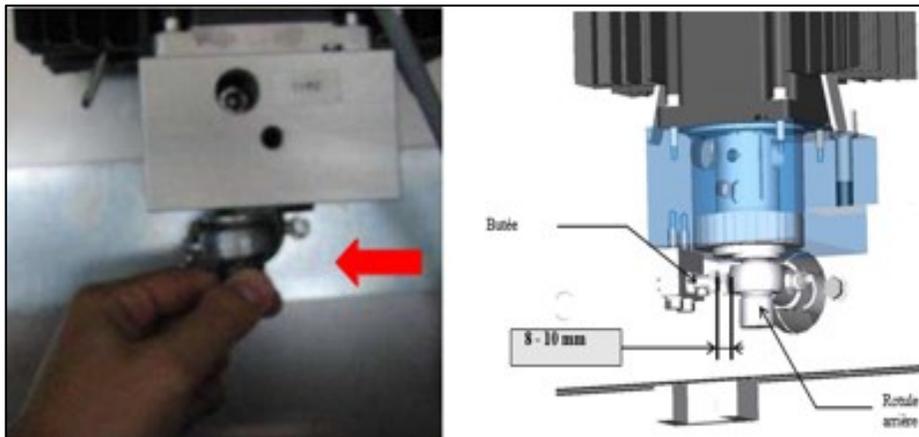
Réglage de la pression de soudure.
